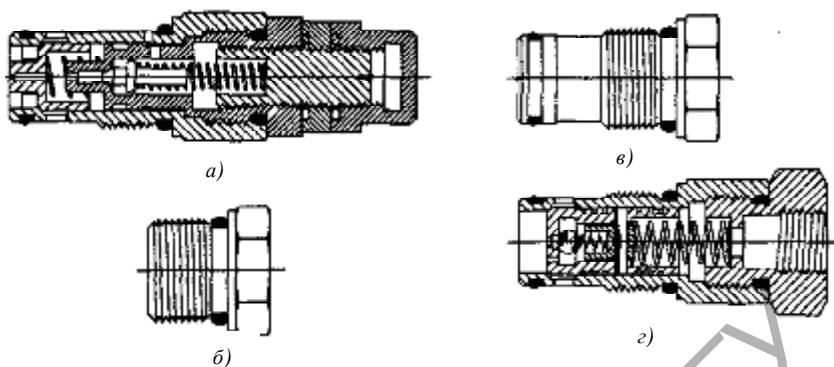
Примерные конструкции клапанов, пробки и заглушки:
